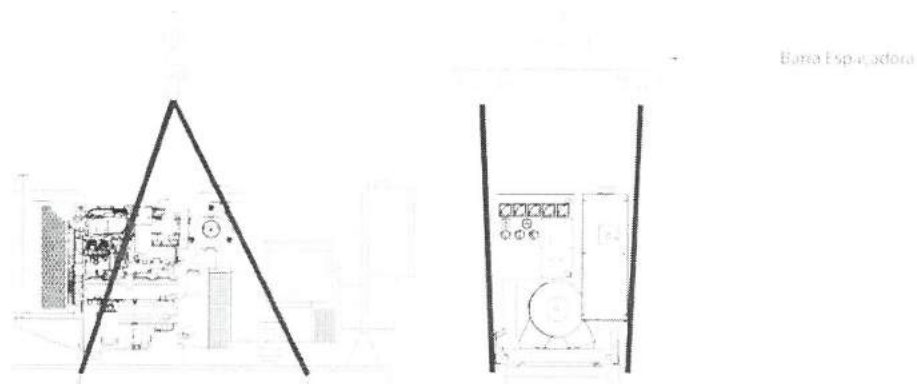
Disposição de elevação adequada para instalação do grupo gerador
